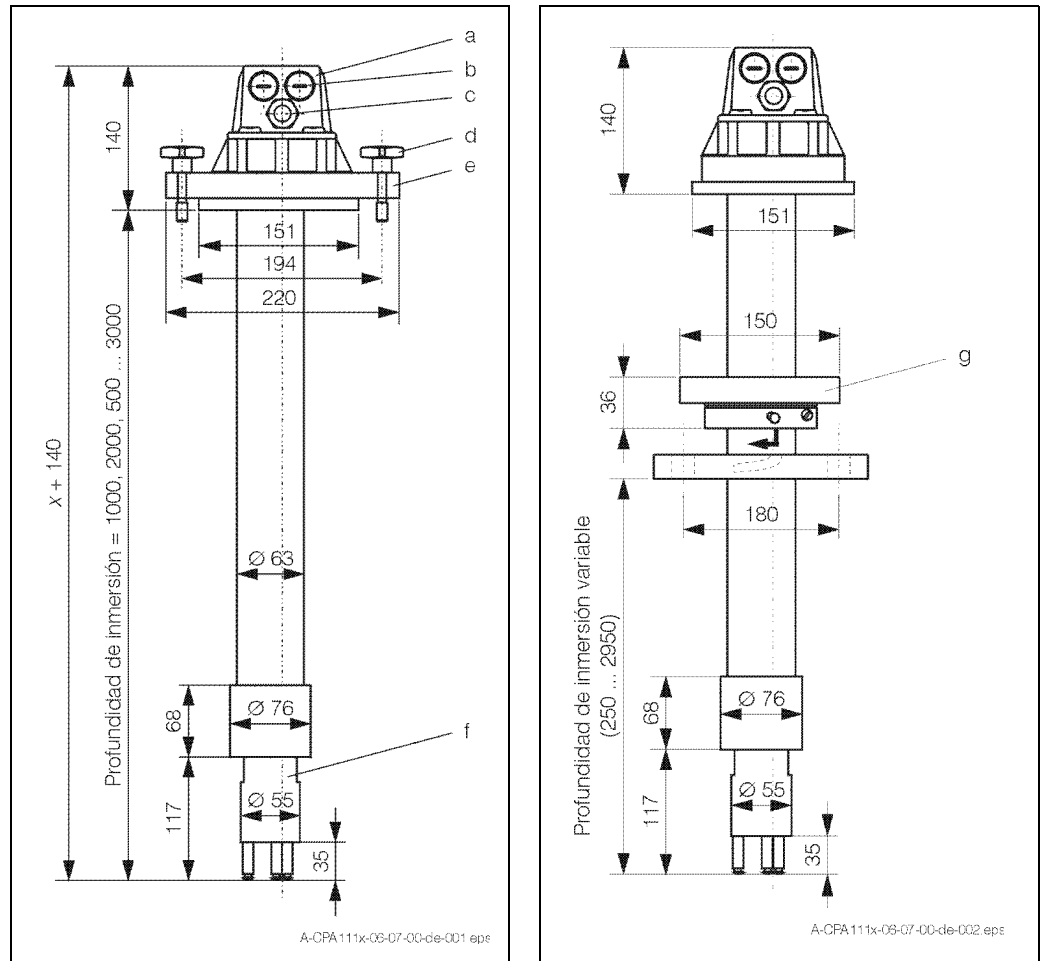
Dimensiones del CPA 111-A/C (izquierda), CPA 111-B (derecha)
